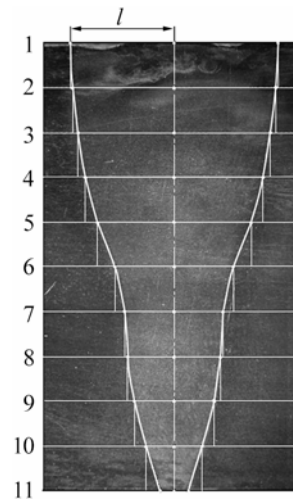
Схема розбиття фотознімка макрошліфа зварного з'єднання.
